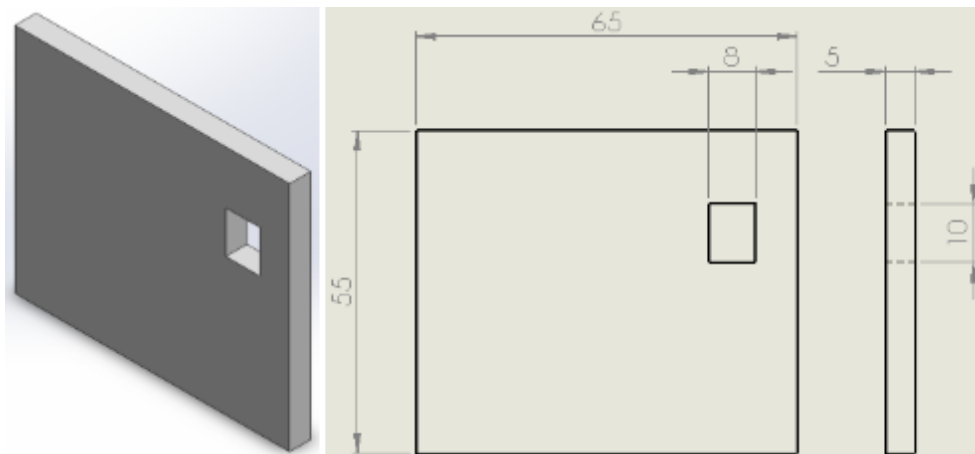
Vista tridimensional y plano de la placa intermedia.
